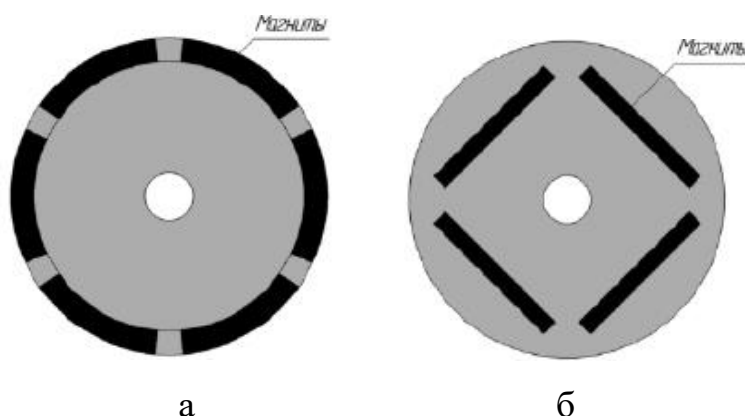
Ротор СДПМ: а – с поверхностной установкой магнитов, б – со встроенными магнитами.
